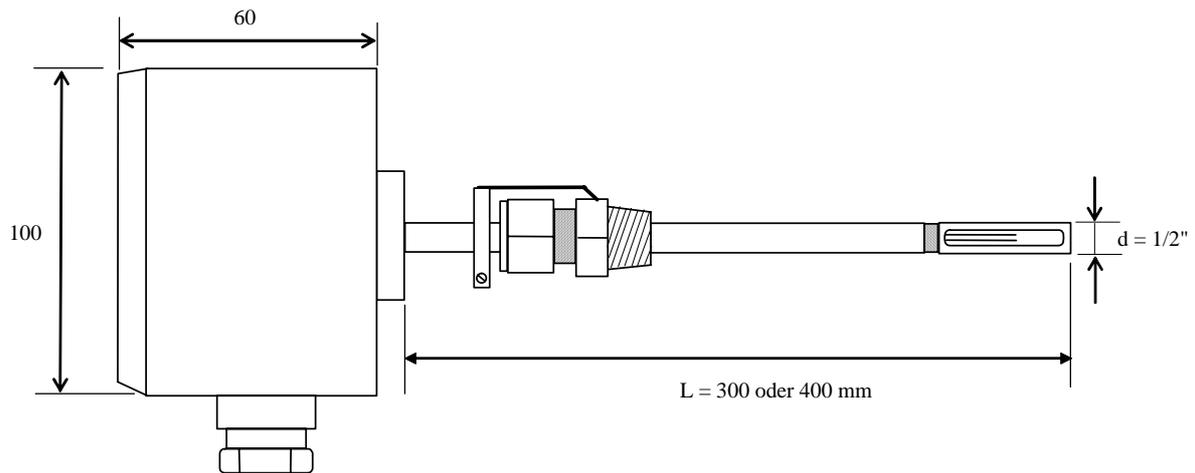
Einpunkt-Eintauch Fühler mit Standard Klemmringverschraubung 1/2" und Zubehör Abstandshalter
